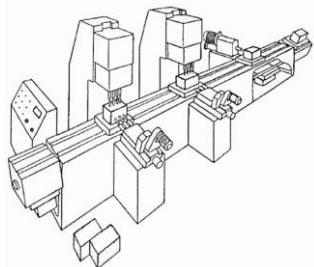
Primjer rotofer i transfer glodaće linije [13]
